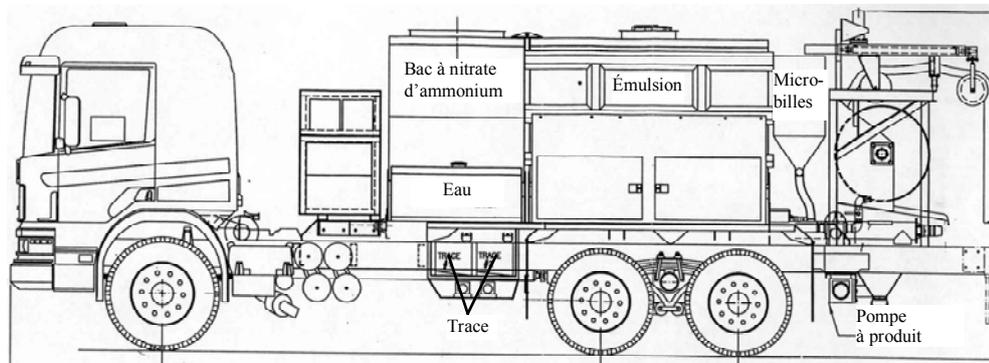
Exemple d'une unité mobile de fabrication d'explosifs
